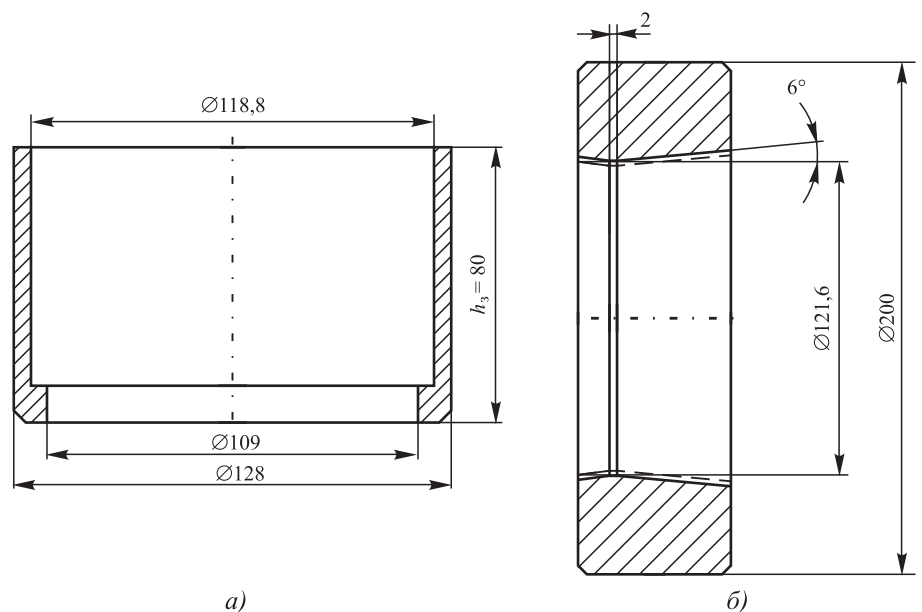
Исходная заготовка (а) и геометрические размеры матрицы для редуцирования (б)
